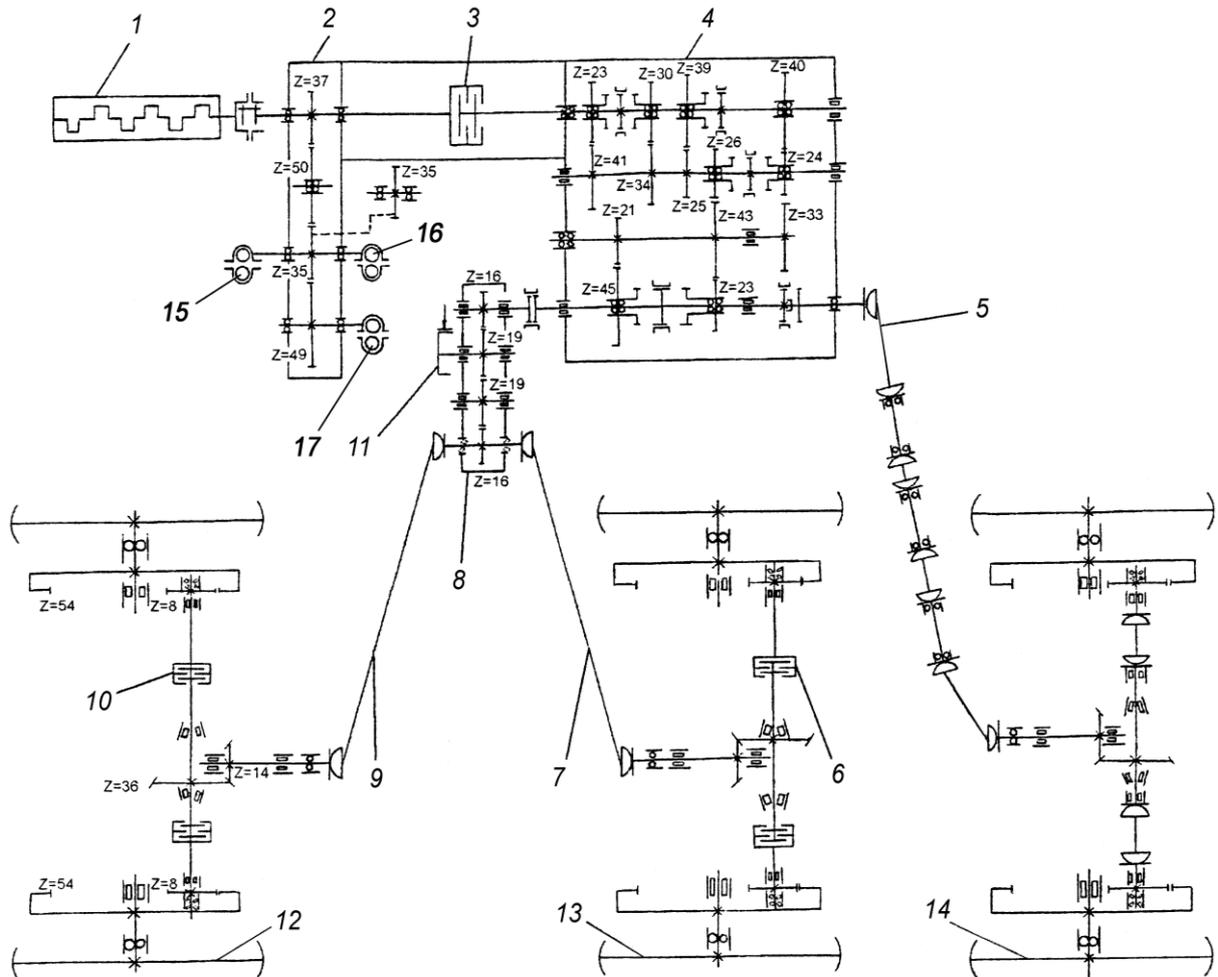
Кинематическая схема автогрейдера ДЗ-98В: 1 – двигатель; 2 – редуктор привода насосов; 3 – сцепление; 4 – коробка передач; 5 – карданная передача; 6, 10 – колесные (рабочие) тормоза; 7, 9 – карданные валы; 8 – раздаточный редуктор; 11 – стояночный тормоз; 12 – задний мост; 13 – средний мост; 14 – передний мост; 15 – насос НШ-50-2; 16 – насос НШ-71А-3; 17 – насос НМШ-25
